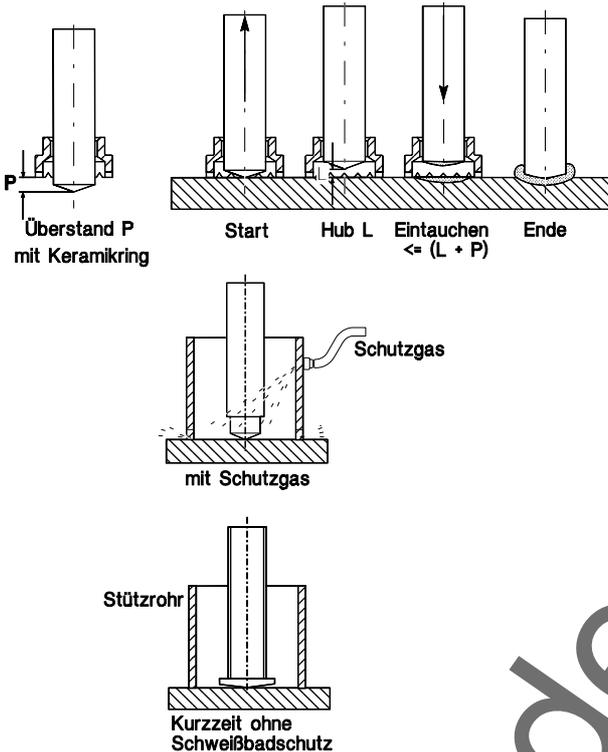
Die Arbeitsphasen beim Lichtbogenbolzenschweißen mit Hubzündung.
